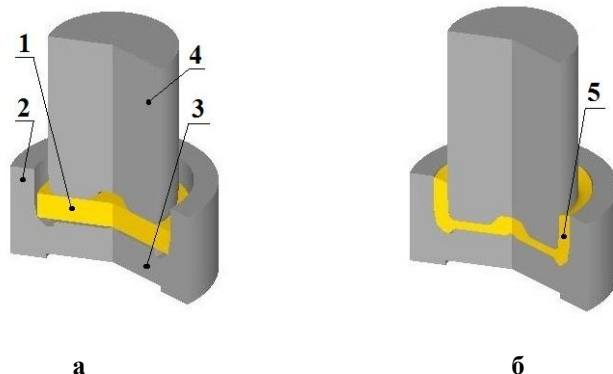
Розрахункові положення деформуючого інструменту: а – положення на початку штампування, б – положення в кінці штампування
